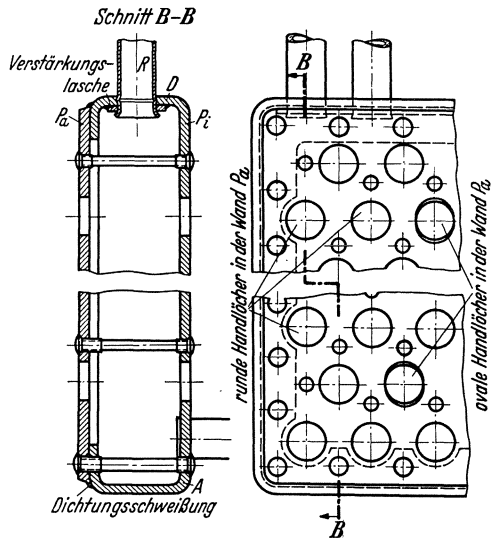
Wasserkammer. Man beachte, daß wie schon früher erörtert wurde, neben runden Handlöchern auch ovale Handlöcher vorgesehen sein müssen, damit die Verschlußdeckel eingebracht werden können.
